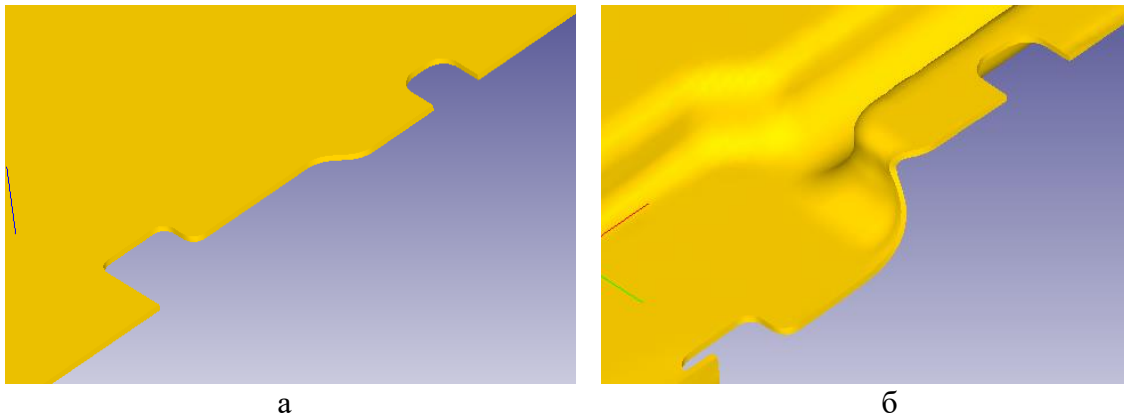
Моделювання деформування заготовки зі скорегованою геометрією: а – елемент контуру заготовки; б – zdeформований напівфабрикат
